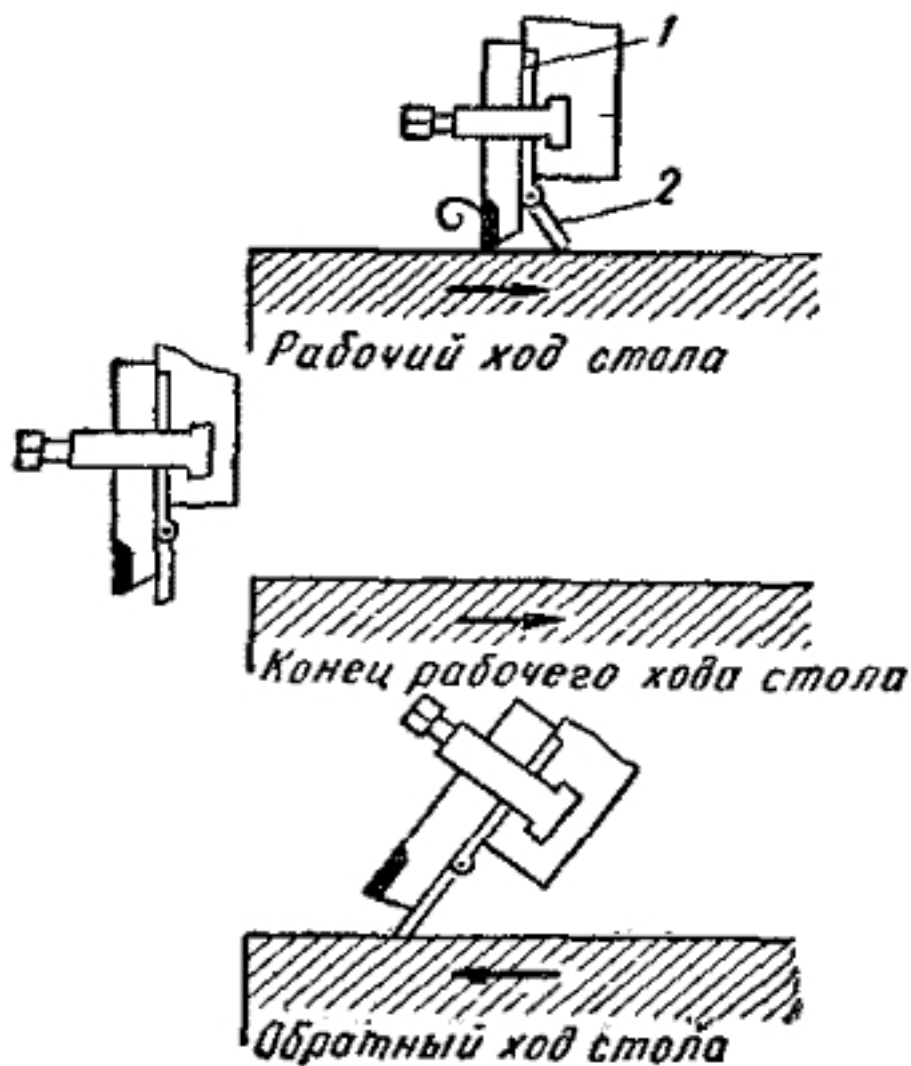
Простейшее приспособление для подъема резца при обратном ходе.
